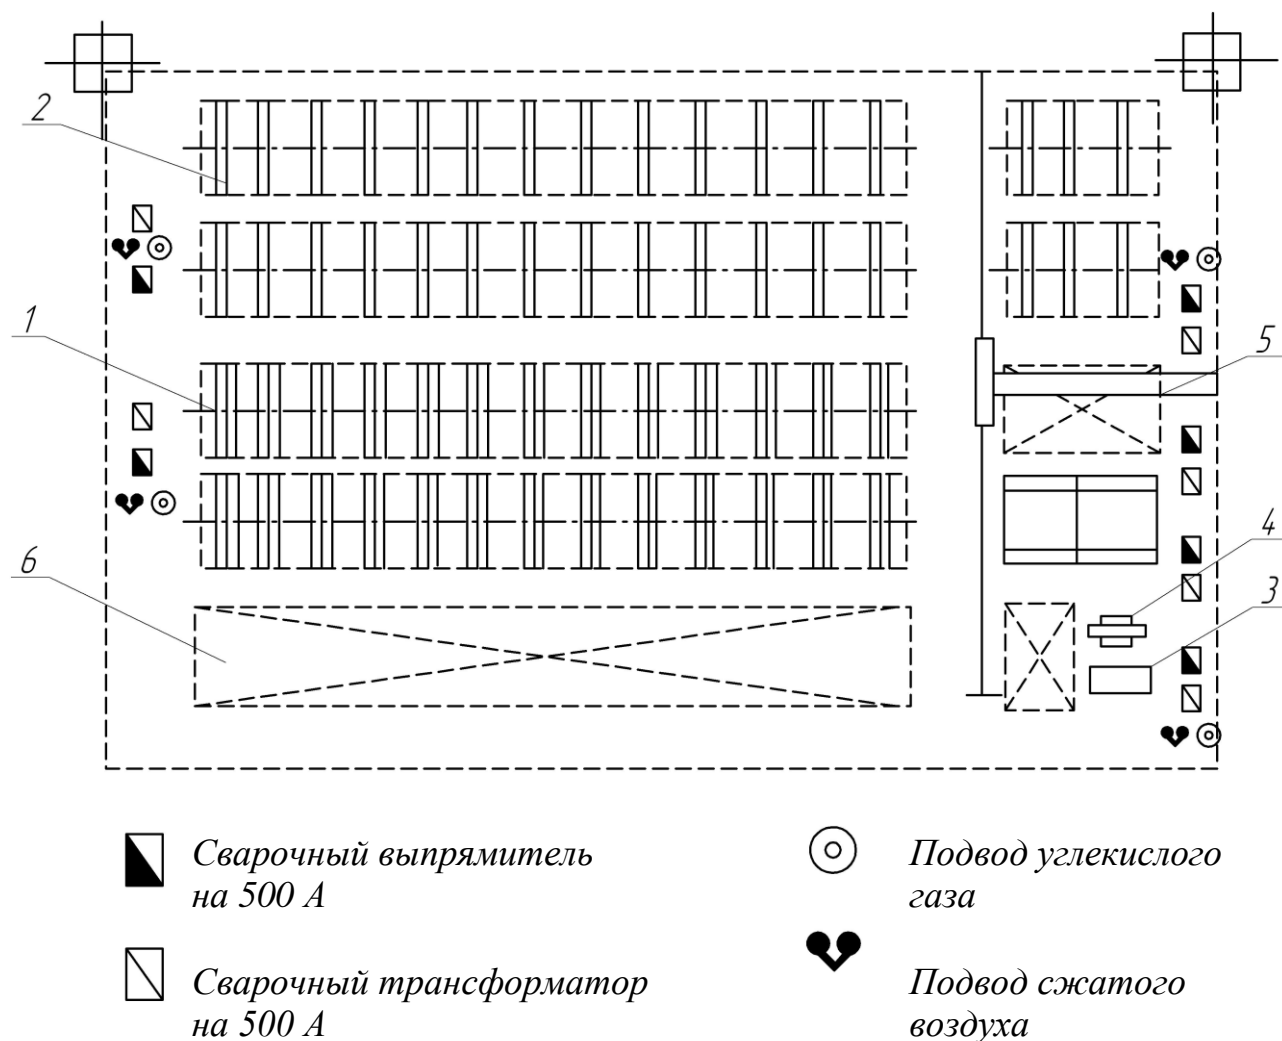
Планировка участка сборки и сварки с применением полукозлового крана:
